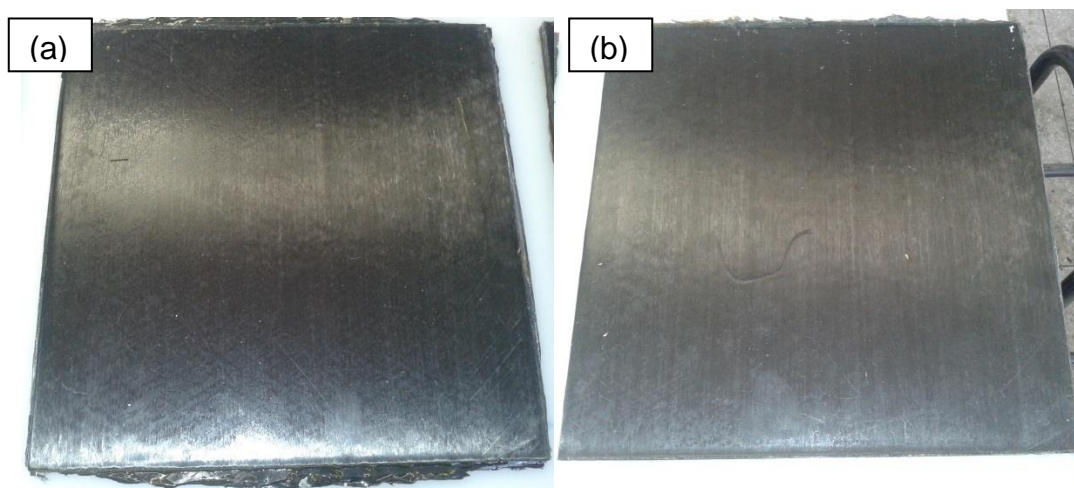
Comparação entre as placas fabricadas: (a) Prensa aquecida com molde de alumínio aberto; (b) Prensa aquecida com molde fechado de alumínio.
